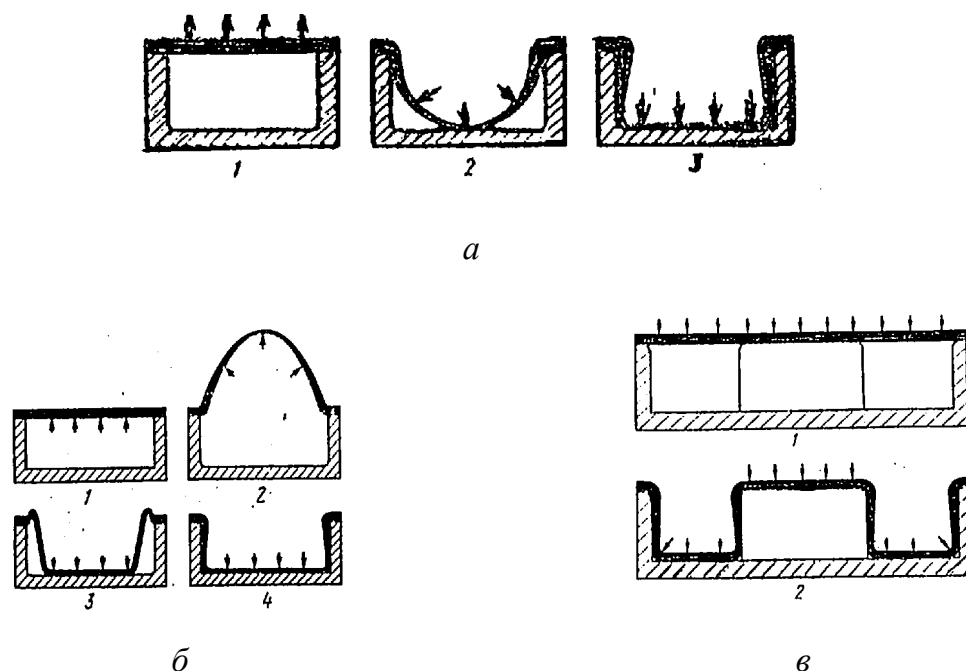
Схемы процессов сверхпластической формовки:
